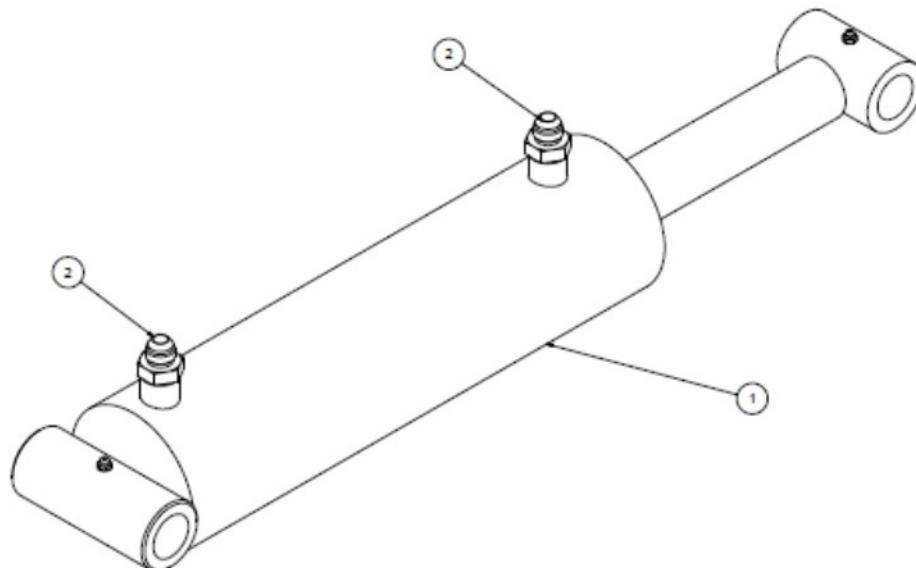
Чертеж цилиндра подъемной руки – 815803
